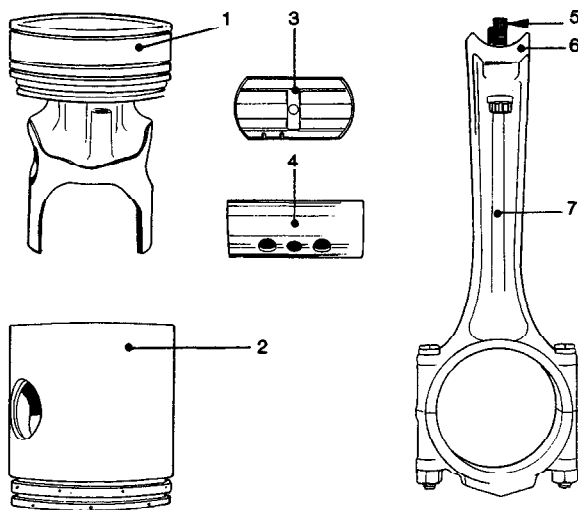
Partes de un pistón con cruceta: 1 corona, 2 falda, 3 cojinete de zapata, 4 pasador de pistón, 5 tornillos, 6 silleta, 7 biela
